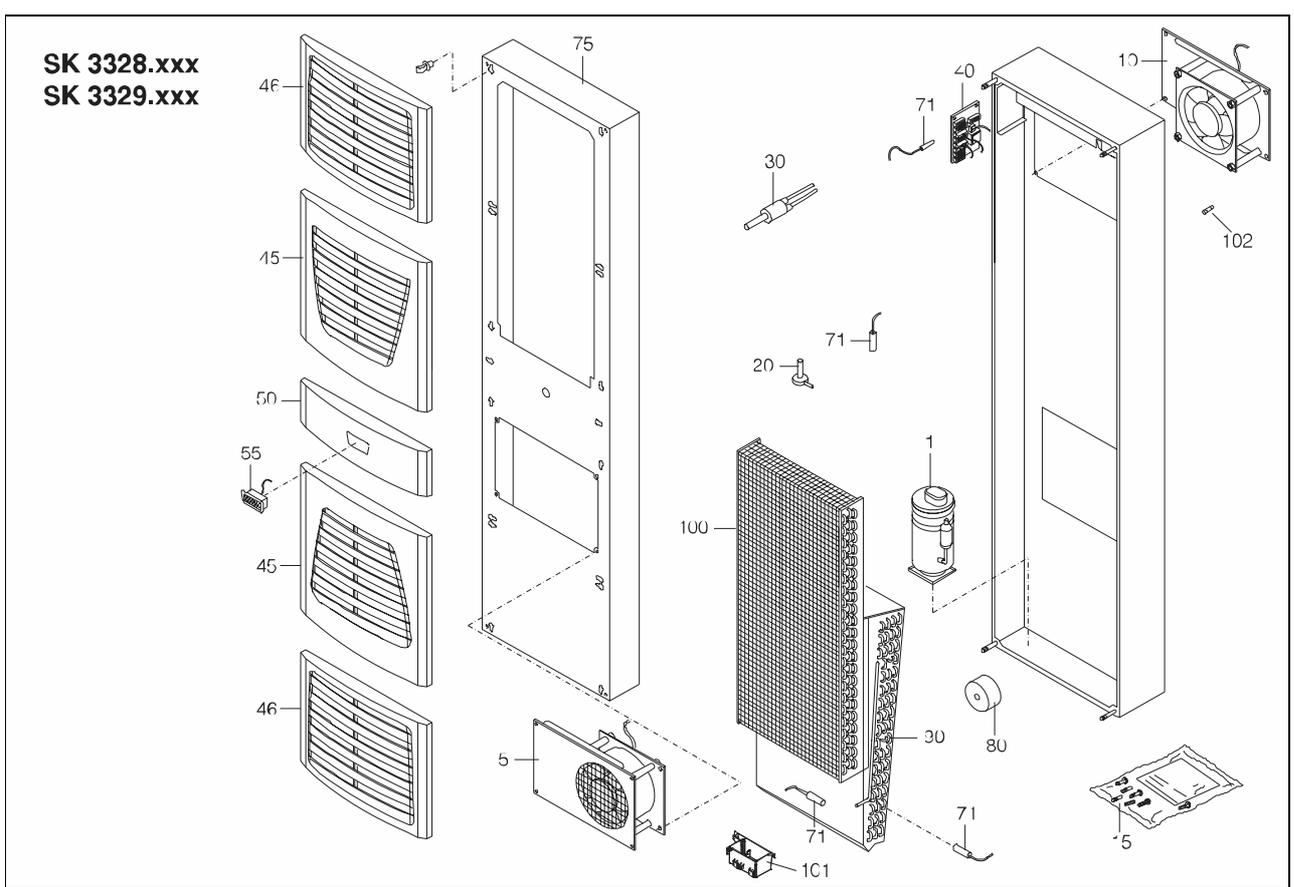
Parti di ricambio per SK 3328.xxx, SK 3329.xxx
